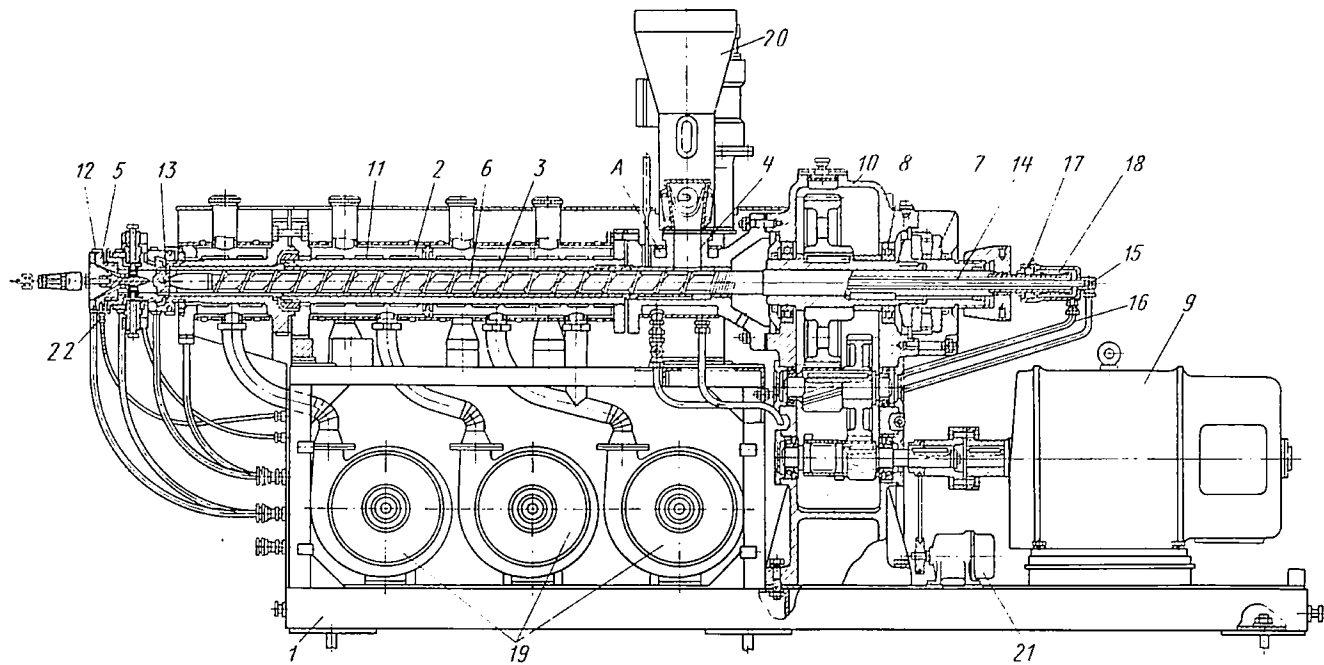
Червячный пресс для получения пленки горизонтальным способом
